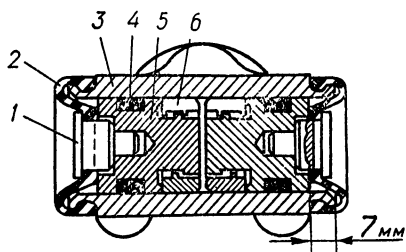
Колесный тормозной цилиндр с устройствами для автоматической регулировки зазоров между колодками и барабаном:
